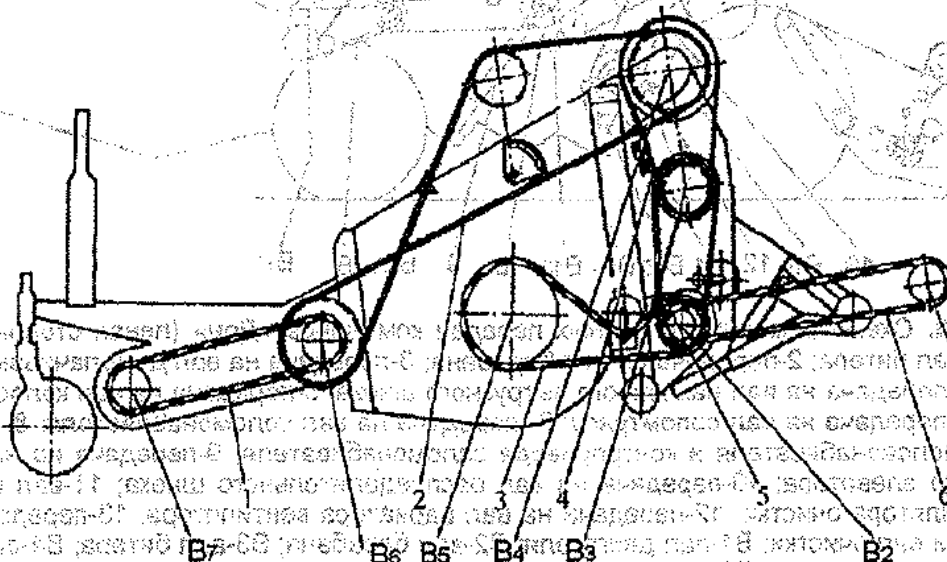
Кинематическая схема платформы-подборщика: 1-передача на ведомый вал транспортера-подборщика; 2-передача на ведущий вал подборщика; 3-передача на вал шнека; 4-передача на верхний вал вариатора; 5-передача на приводной вал; 6-передача на верхний вариатора; В1-вал трансмиссионный; В2-вал приводной; В3-вал нижний вариатора; В4-вал верхний вариатора; В5-вал шнека; В6-вал ведущий подборщика; В7-вал ведомый подборщика
